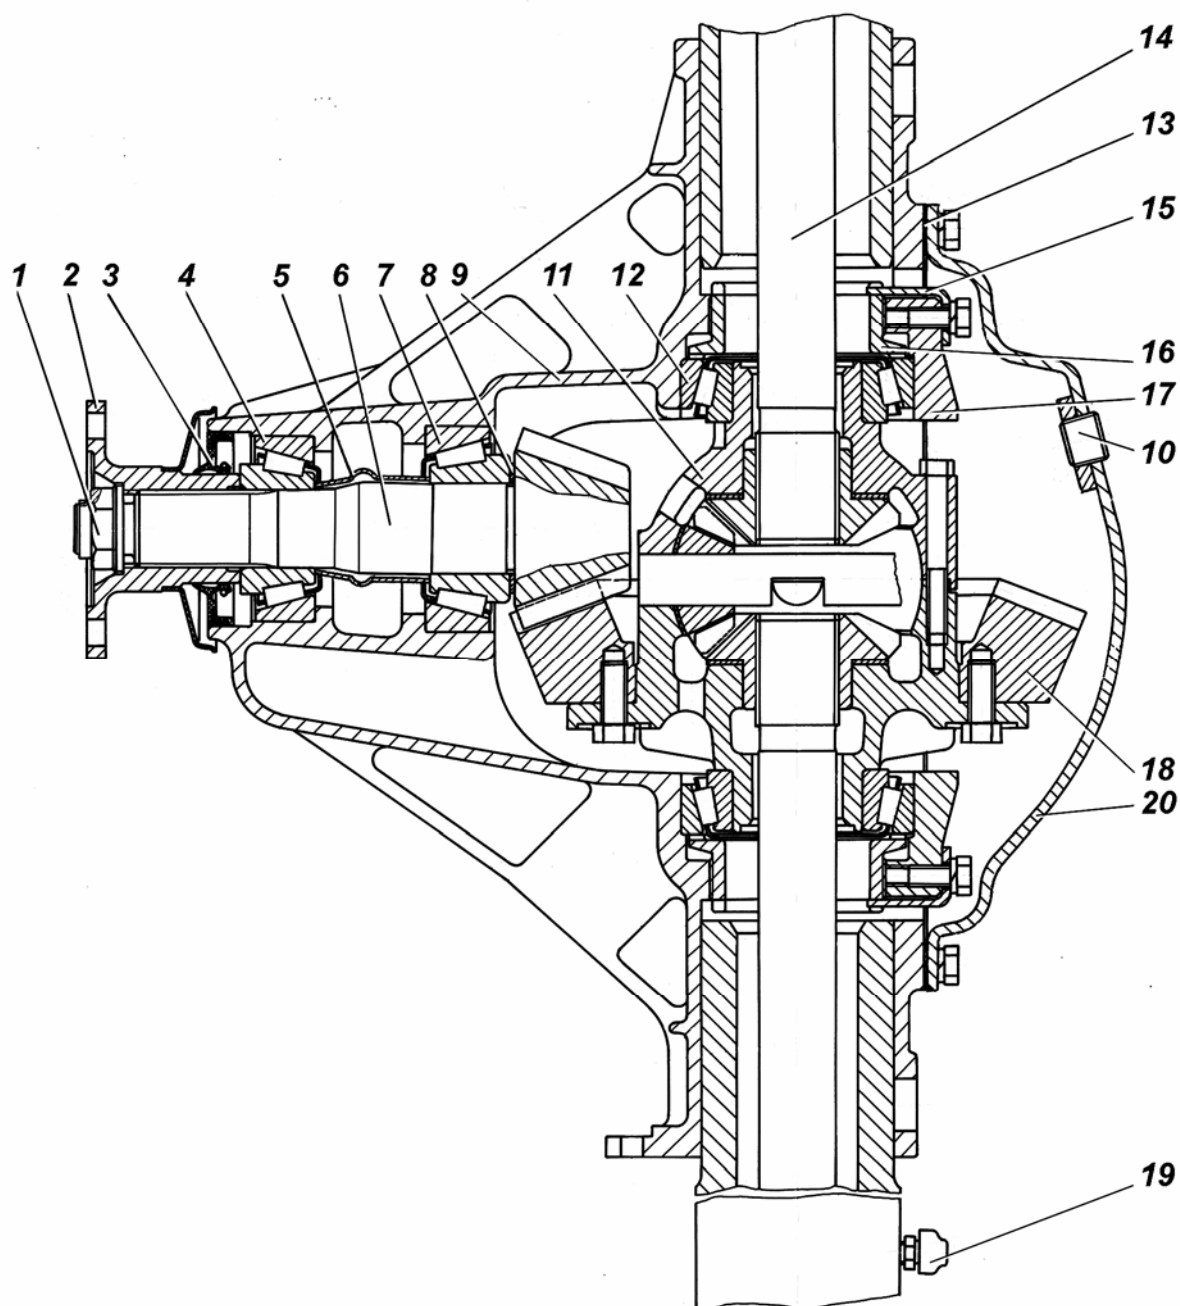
Передний ведущий мост автомобиля типа 4x4 (средняя часть): 1 – гайка; 2 – фланец ведущей шестерни; 3 – манжета; 4, 7 и 12 – подшипники; 5 – распорная втулка; 6 – ведущая шестерня; 8 – регулировочное кольцо; 9 – картер; 10 – пробка маслозаливного отверстия; 11 – дифференциал; 13 – прокладка; 14 – вилка внутренняя; 15 – стопорная пластина; 16 – гайка подшипников дифференциала; 17 – крышка подшипника дифференциала; 18 – ведомая шестерня; 19 – сапун; 20 – крышка картера
